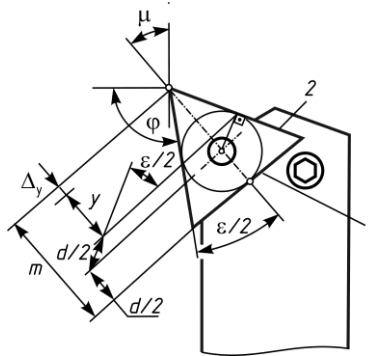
Схема розрахунку похибки базування пластини в кутовий паз
